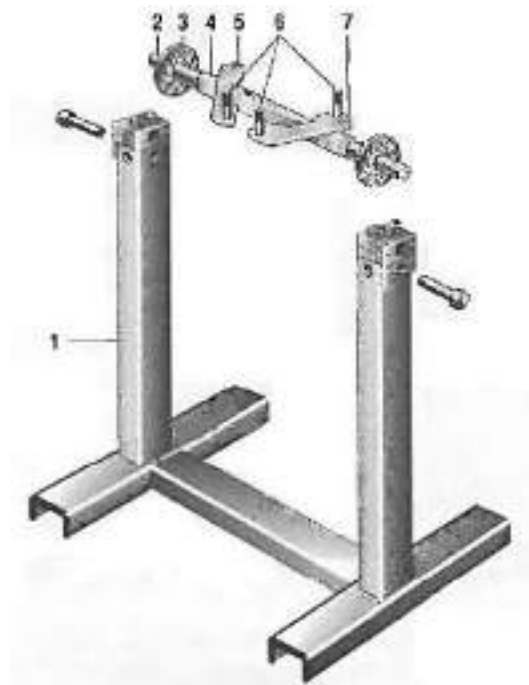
Траверса для коробки передач: 1 – Універсальний стенд; 2 – Цапфи; 3 – Диск; 4 – Траверса; 5 – Ліва пластина; 6 – Болт (3 шт.); 7 – Права пластина; 8 – Гайка шпильки коробки передач; 9 – Гайка болта (6 шт.)
